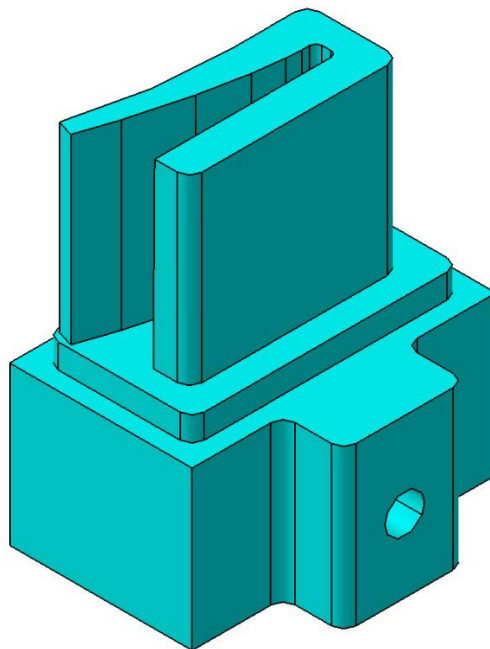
Detail- drážka vymezení posuvu středového zobáčku
